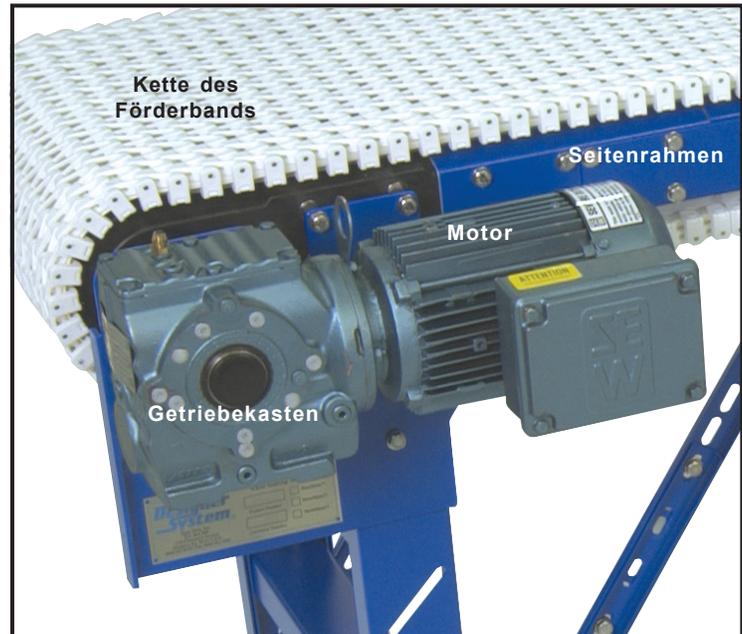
Hohlwellen-Antriebsmotor, horizontal montiert
